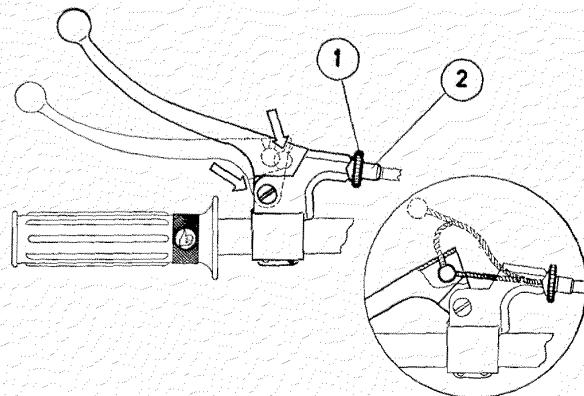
Mando embrague: Reglaje, engrase y cambio de cable.
